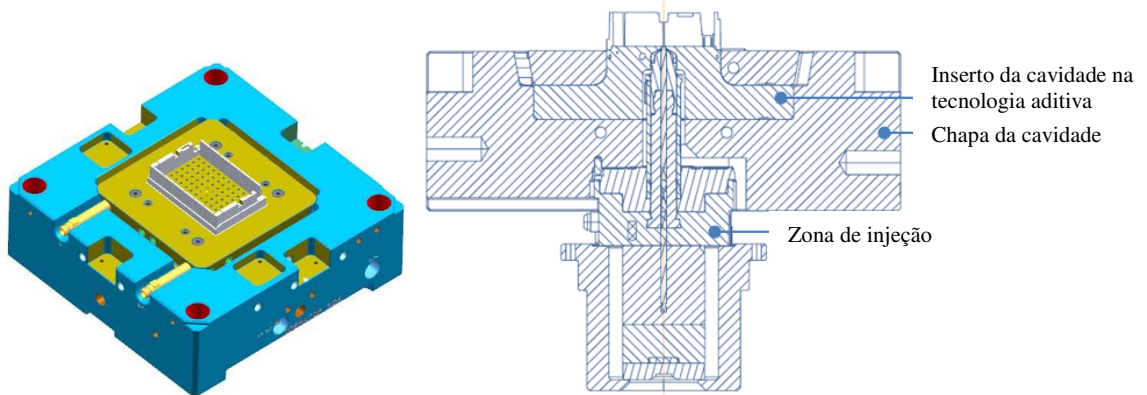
Vista e corte transversal do lado da injeção do molde de fabrico aditivo
